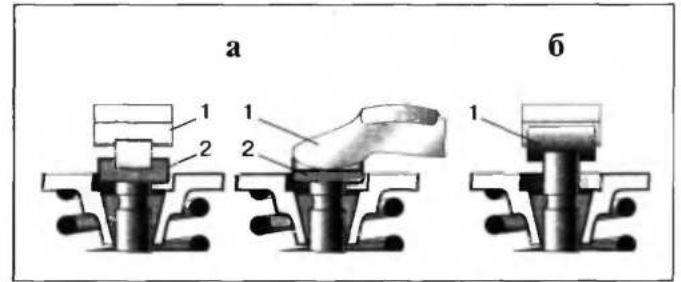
Способы передачи усилия с рычага на клапан: а — через шайбу-толкатель; б — непосредственно (применяется редко); 1 — рычаг; 2 — шайба-толкатель
